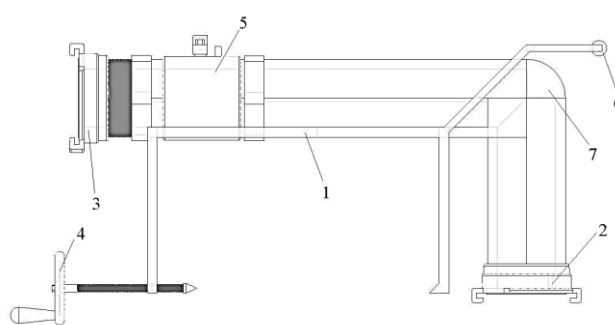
Конструкция перекрывной рукавной задержки: 1 – несущая рама; 2, 3 – соединительная муфтовая головка Ø 77 мм; 4 – регулировочный винт; 5 – шаровой кран; 6 – ролик; 7 – корпус
